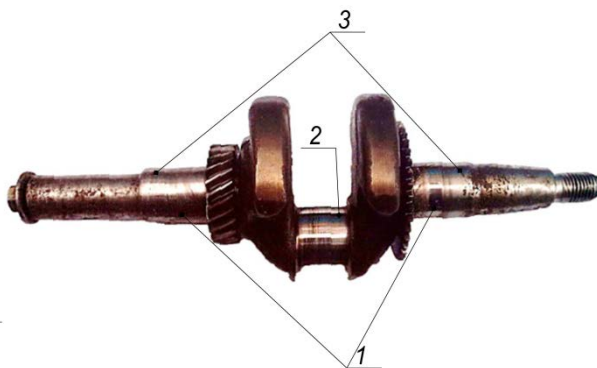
Дефекты коленчатого вала двигателя Briggs&Stratton модели 115400: 1 – износ поверхностей под подшипники, 2 – износ шатунной шейки, 3 – износ поверхностей под сальники
